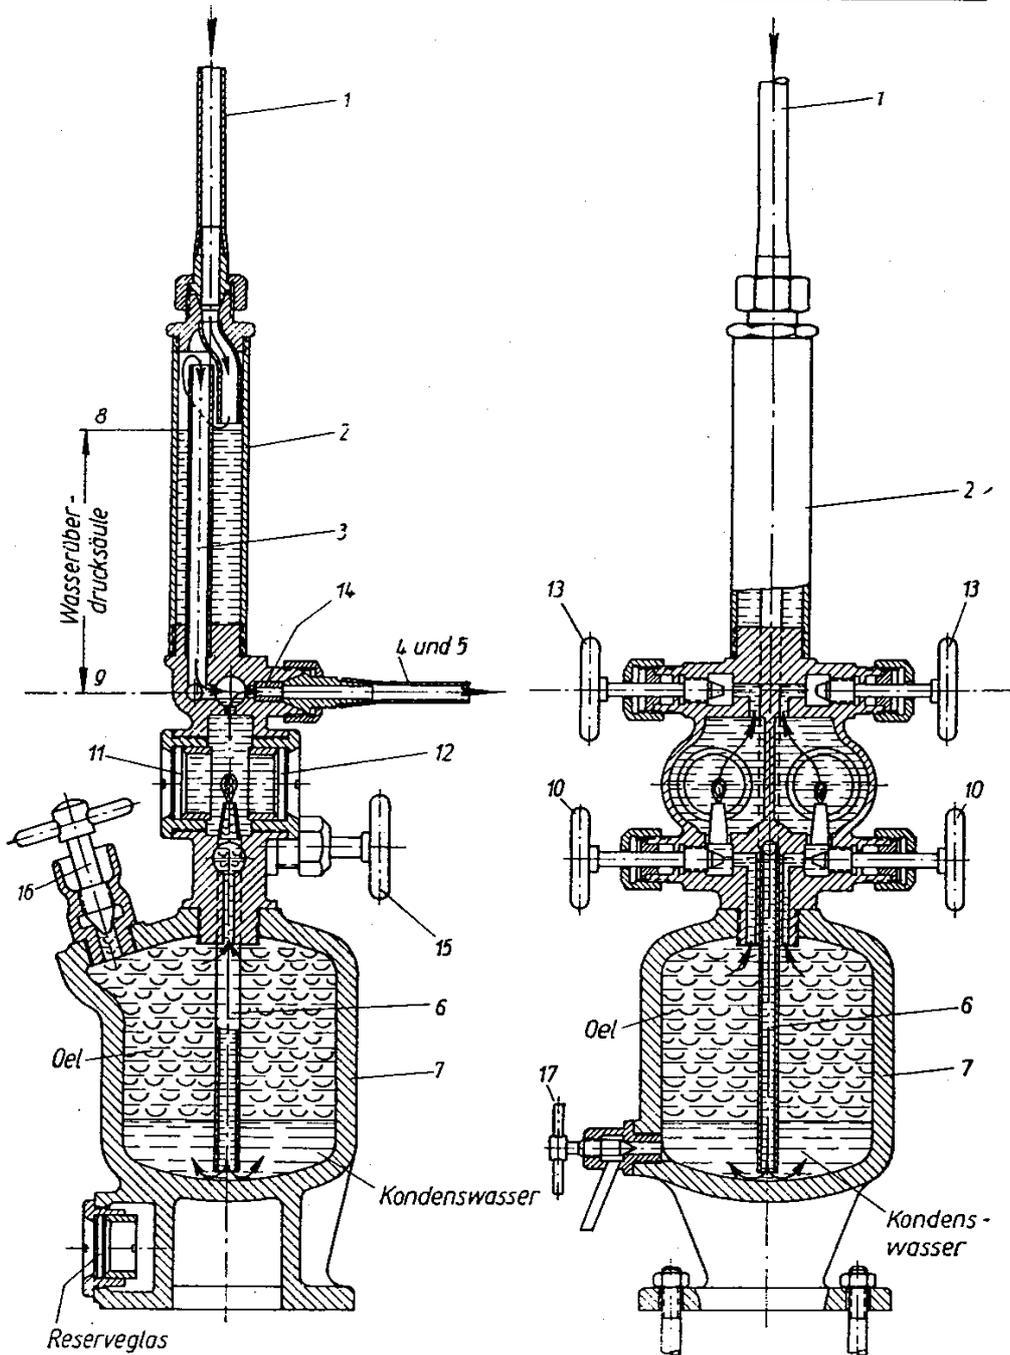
De Limon-Sichtöler für Schieber und Zylinder
